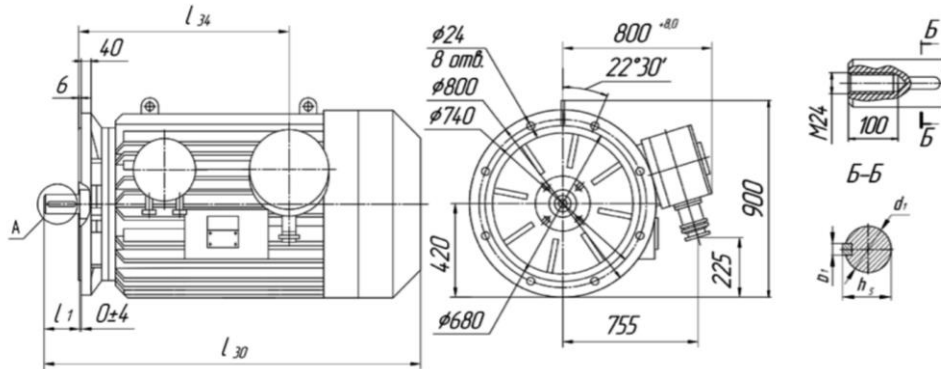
Габаритные и присоединительные размеры двигателей IM3001.
